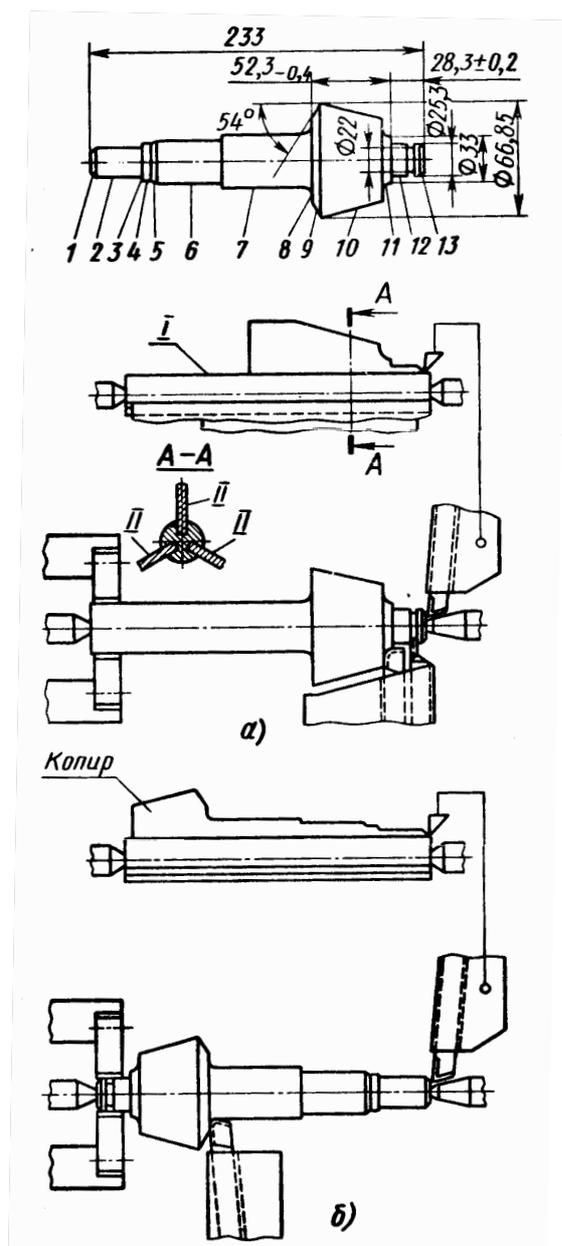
Наладка копировального полуавтомата для обработки конической валшестерни
